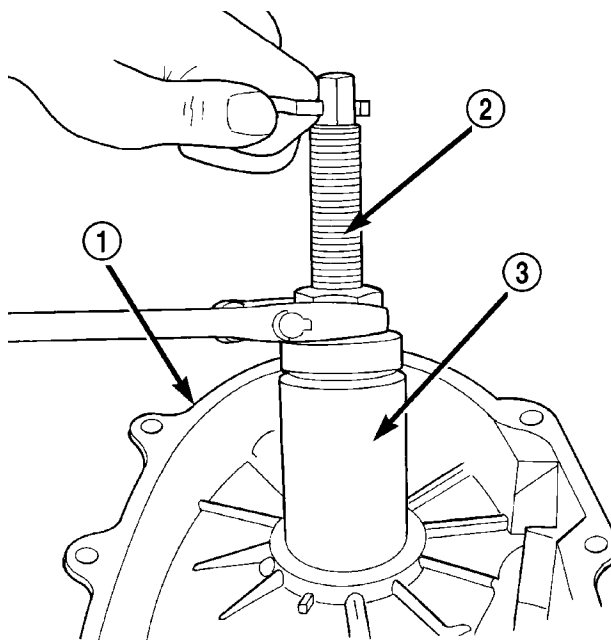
Desmontaje del cojinete trasero del eje transmisor
